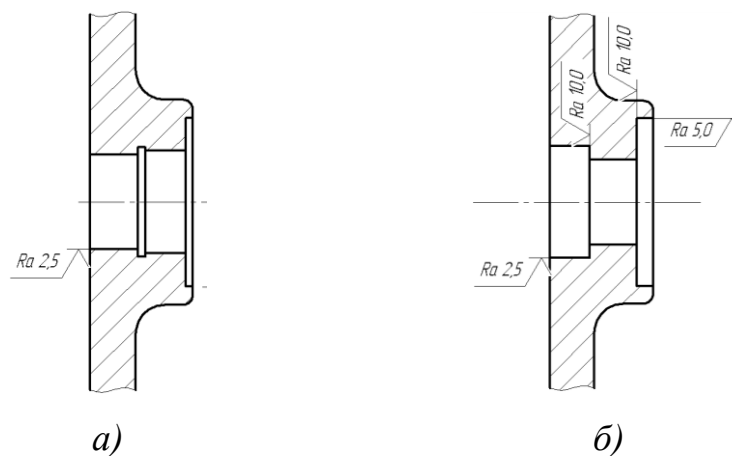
Фрагменти поверхонь корпусної деталі:
